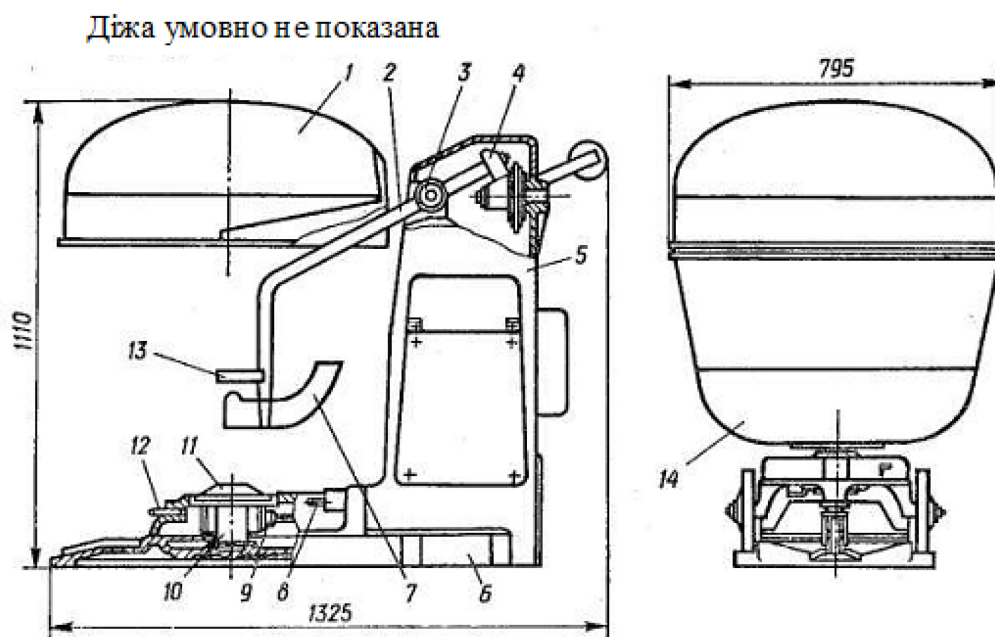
Тістомісильна машина ТММ-1М: 1 – огорожа; 2 – важіль мішалки; 3 – поворотний кулак; 4 – кривошип; 5 – корпус; 6 – фундаментна плита; 7 – лопать; 8, 12 – штирі; 9 – квадратне гніздо; 10 – редуктор; 11 – конічний диск; 13 – направляюча лопатка; 14 – діжа.
